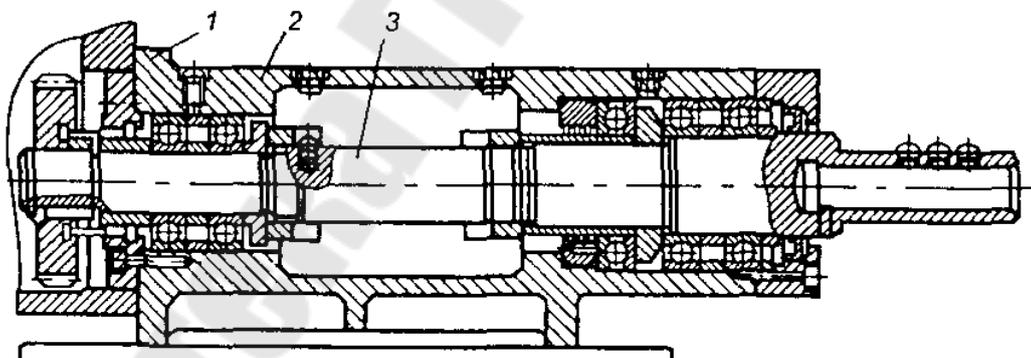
Конструкция сверлильной бабки агрегатного станка
